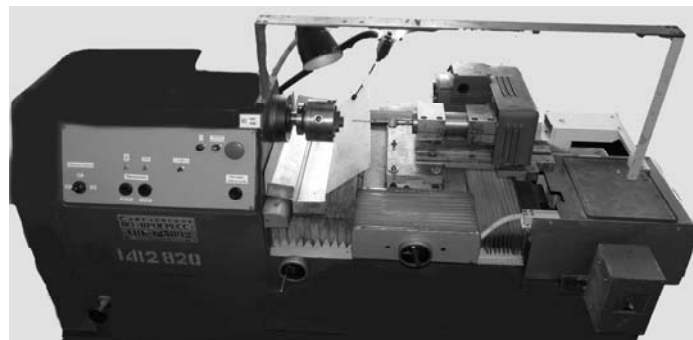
Внешний вид модернизированного токарного станка ТПК-123В112
